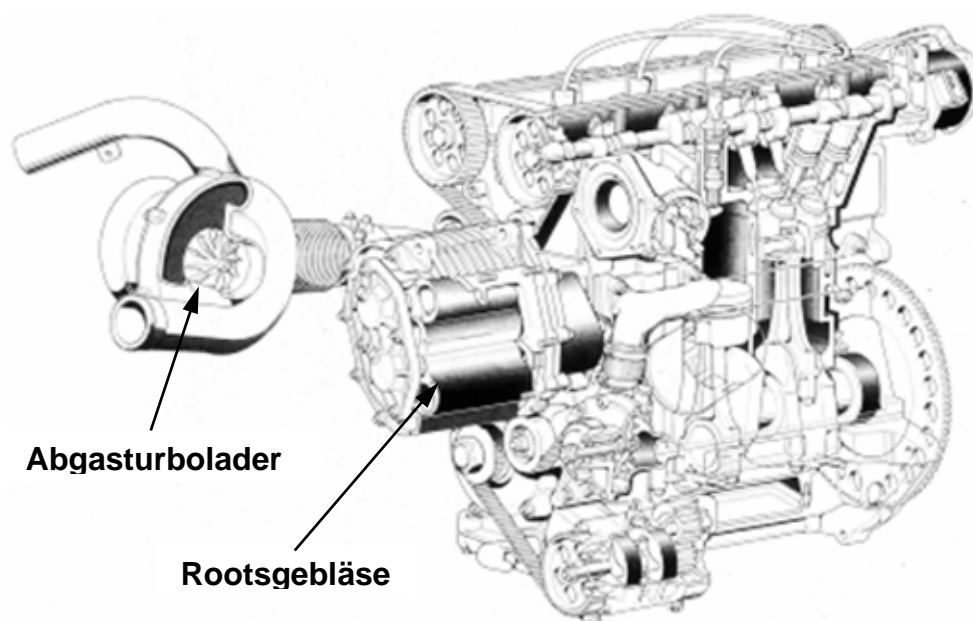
Motor des Gruppe B Rallyfahrzeuges Lancia Delta S4 mit kombinierter mechanischer- und Abgasturboaufladung
